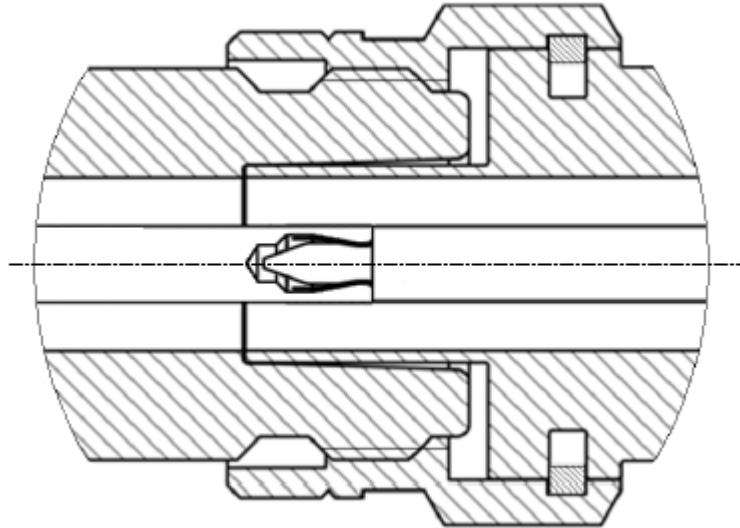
Соединители тип N (розетка слева, вилка справа)
